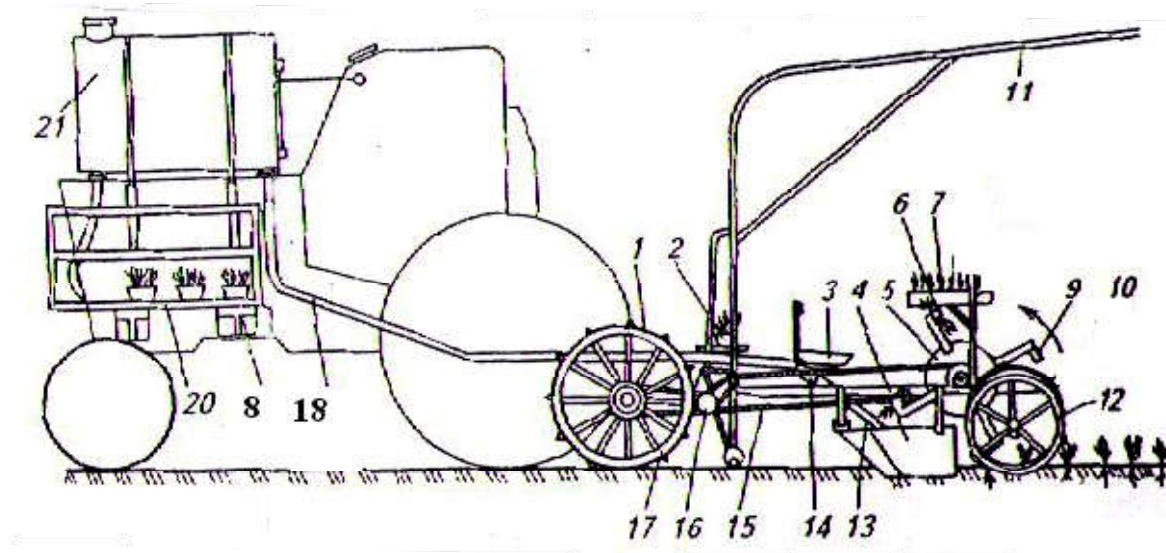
1 – опорно-приводное колесо; 2 - помост; 3 – сиденье; 4 - сошник; 5 – посадочный диск; 6, 9 - рассадодержатели; 7, 8 – ящики с рассадой; 11 - бак для воды; 12 – прикатывающие катки; 13 – поливная труба; 14- поливной бачок; 15, 17 – цепные передачи; 16 - редуктор; 18 – сливная труба; 20 – стеллаж; 21 – бак.
